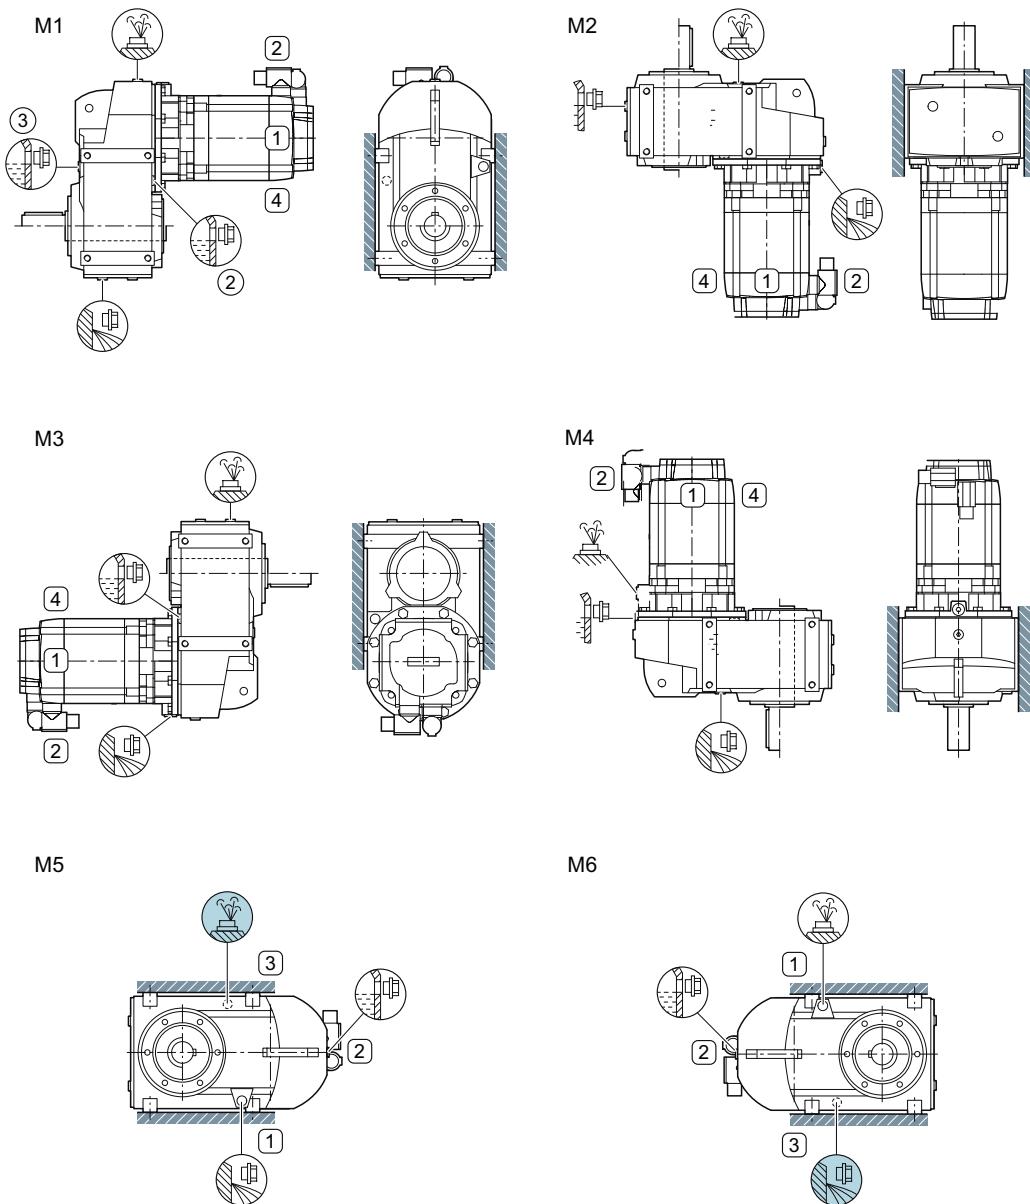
Einbaulagen für Servo-Flachgetriebemotoren FZ und FD, Fußausführung, Baugrößen 39 - 129, 2-stufig und 3-stufig
